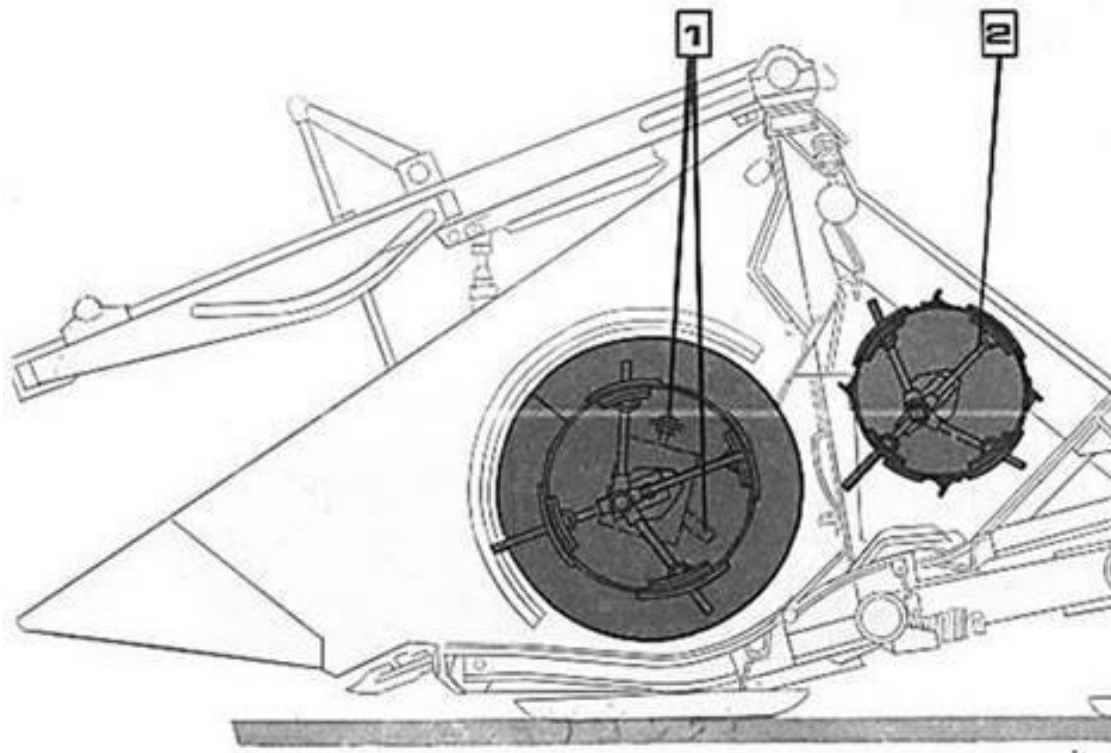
Схема регулировки шнека жатки и механизма проставки:
